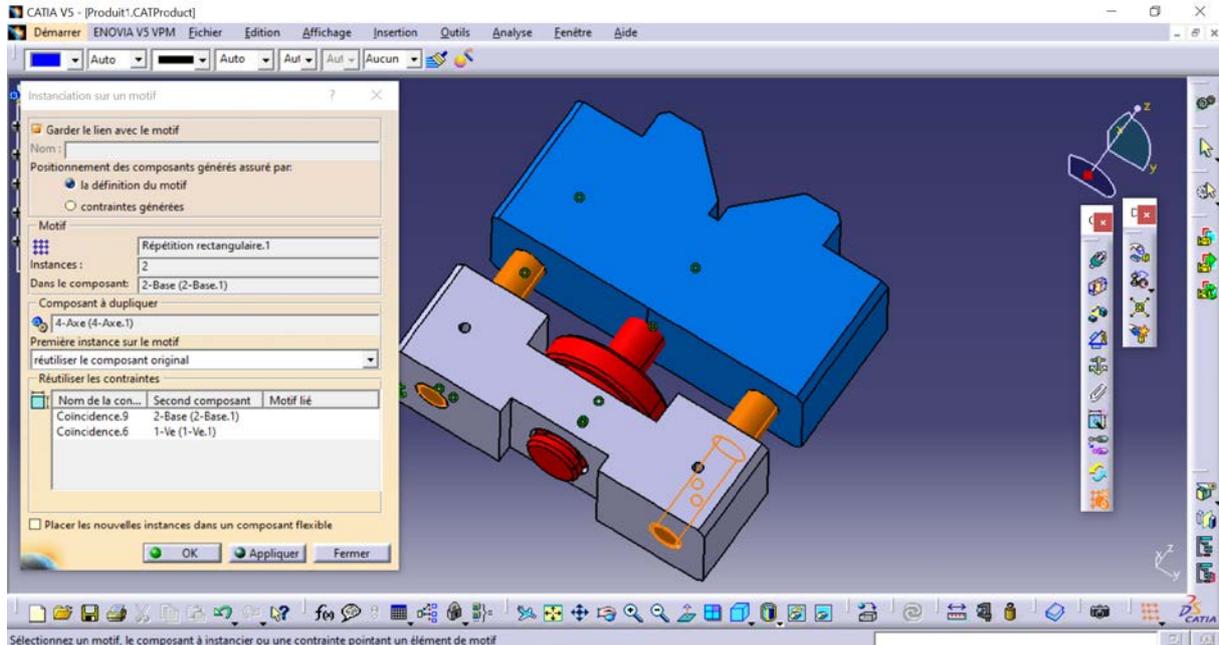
Assembly Design (Insertion du deuxième Axe 4) [1], [2]
